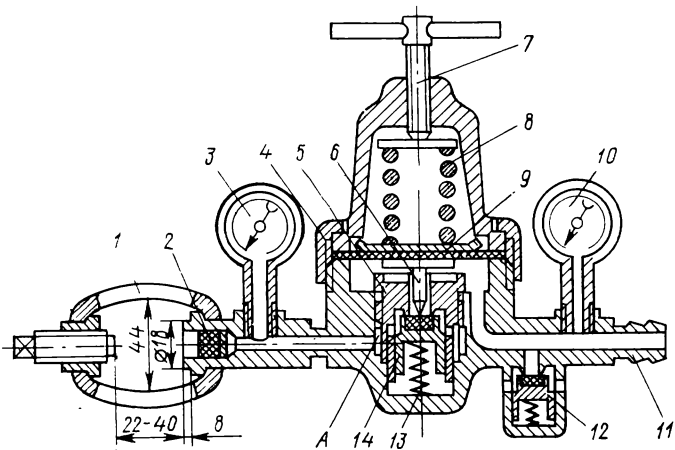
Схема устройства редуктора типа ДАП-1 для ацетилена.
